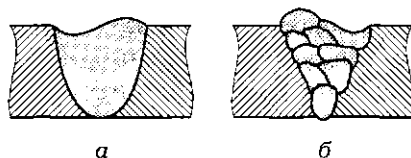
Неполное заполнение разделки кромок однопроходного [а] и многопроходного [б] стыковых сварных швов
